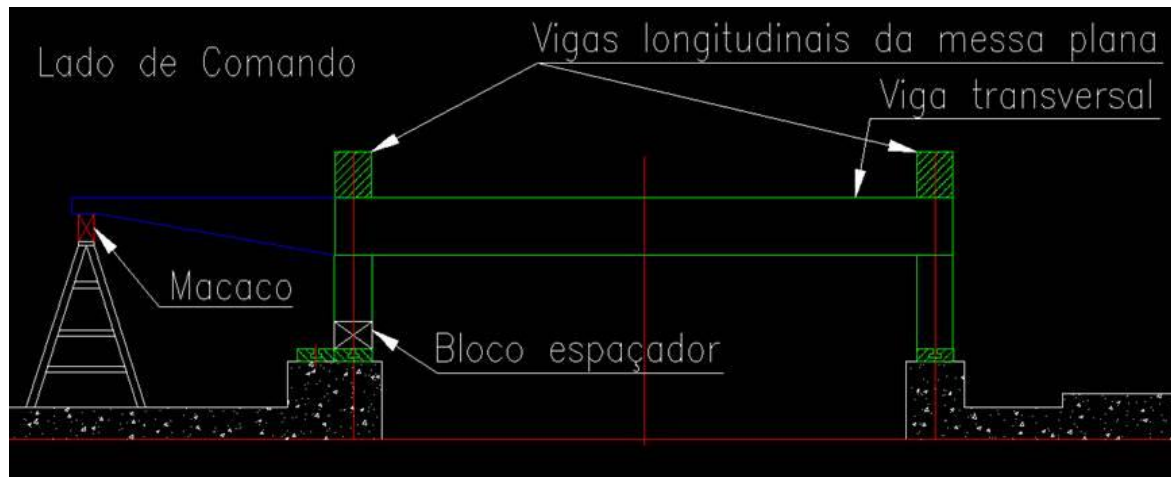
Ilustração de uma mesa plana com estrutura tipo porter bar
